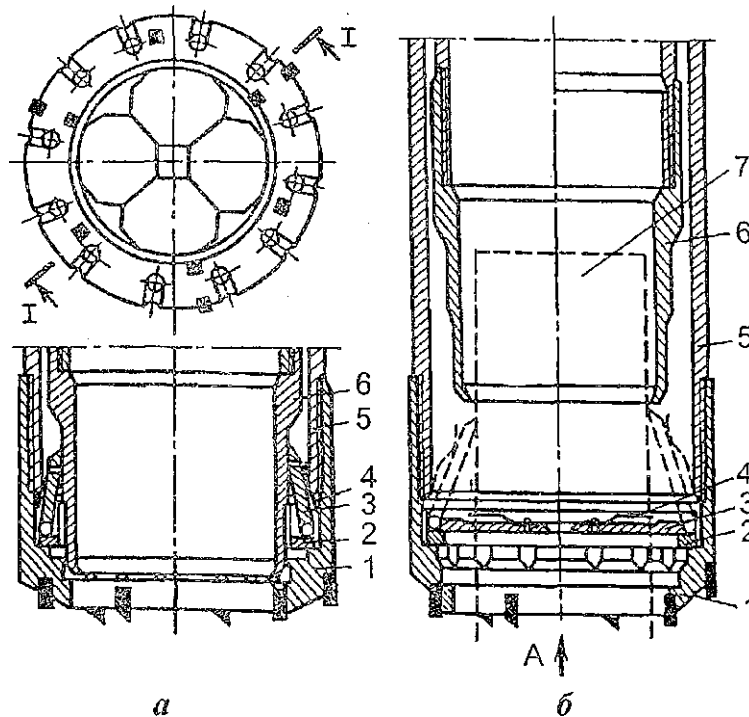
Схема устройства кернорвателя закрытого типа конструкции ТПИ: а - в процессе бурения; б - при заклинивании и срыве керна: 1 - коронка; 2 - кольцо-корпус кернорватель-ного устройства; 3 - кернозахватывающие элементы клапанного типа; 4 - отбойная пружина; 5 - наружная колонковая труба; 6 - стакан керноприемника; 7 - керн
